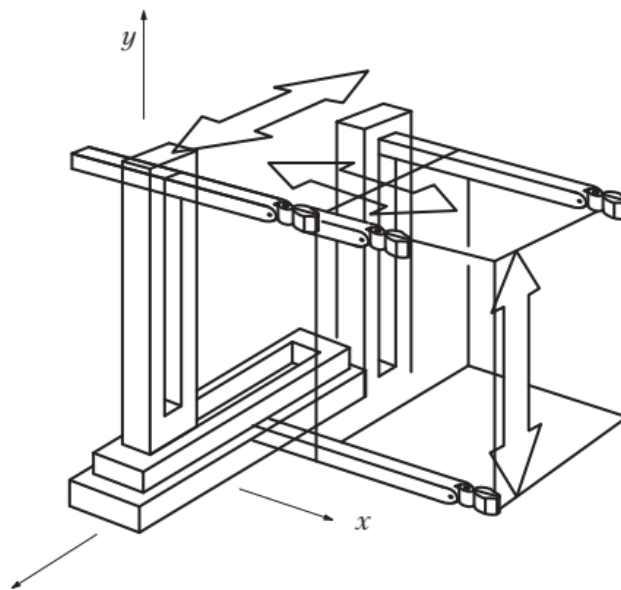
Манипулятор с поступательными исполнительными движениями
